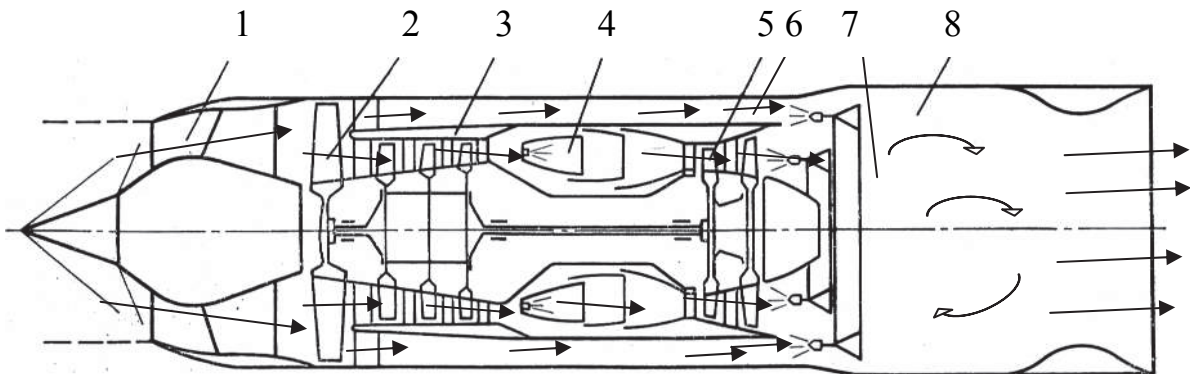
Схема двухконтурного турбореактивного двигателя с форсажной камерой (ДТРДФ)
